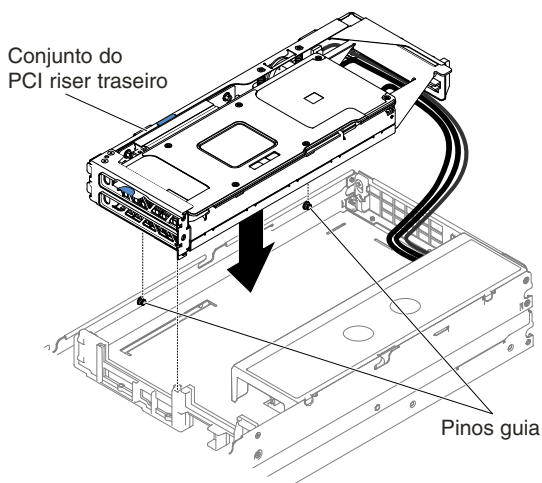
Instalação do conjunto do compartimento da placa riser PCI traseiro
